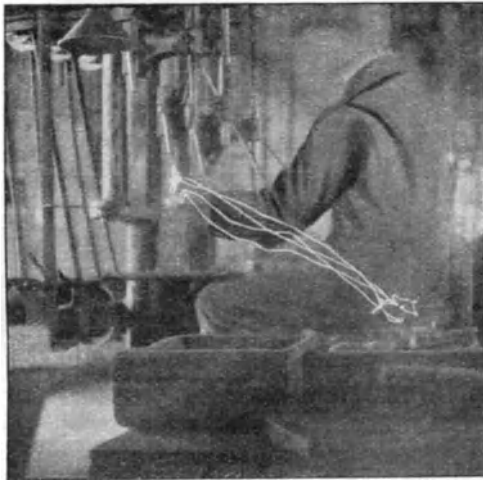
Komplizierte Bewegungen vor Einführung der wissenschaftlichen Betriebsführung. Das zu bearbeitende Werkzeug wird während des Transportes vom Kasten zur Maschine erst in die richtige Lage gebracht. Das Bild zeigt geistige Unentschlossenheit des Arbeiters bei Ausführung der Arbeitsbewegung. Anstatt das aus dem Werkzeugkasten herausgenommene Stück ohne Bedenken gerade und sicher zur Maschine zu führen, wird unterwegs gezaudert und die Hand unentschlossen vorwärts und rückwärts geführt.
